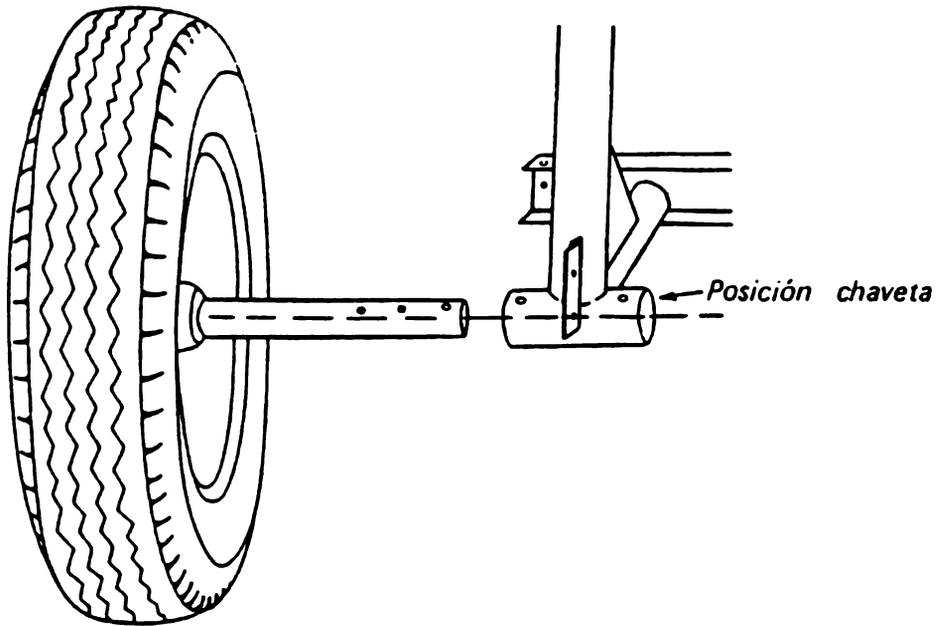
DESPIECE DEL SISTEMA DE RODADO
